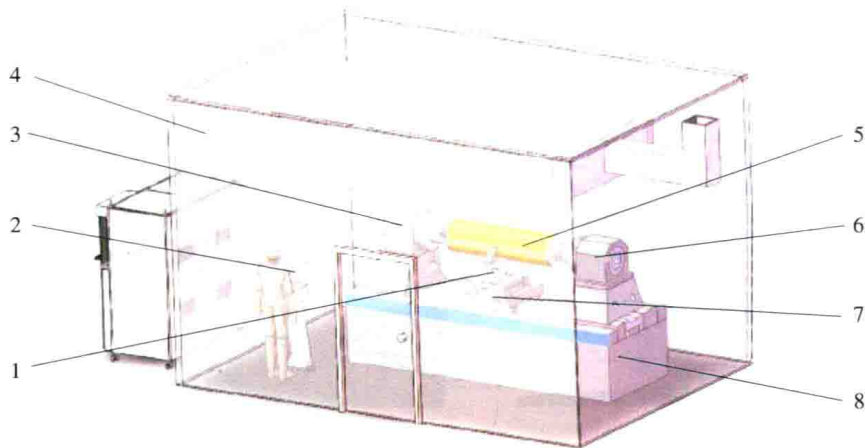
大尺寸微结构模辊超精密加工机床整体布局
